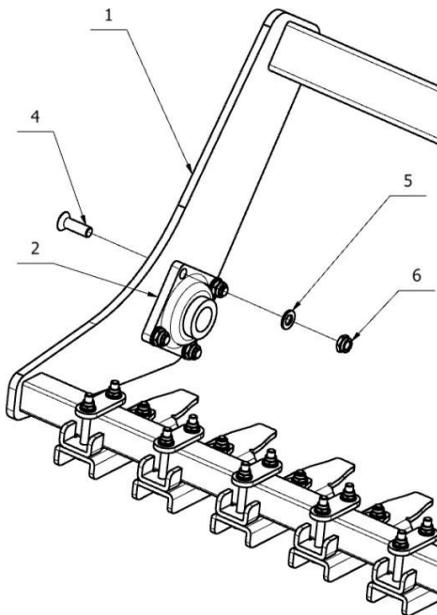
Dachwalze Ø500mm – Lagermontage.
